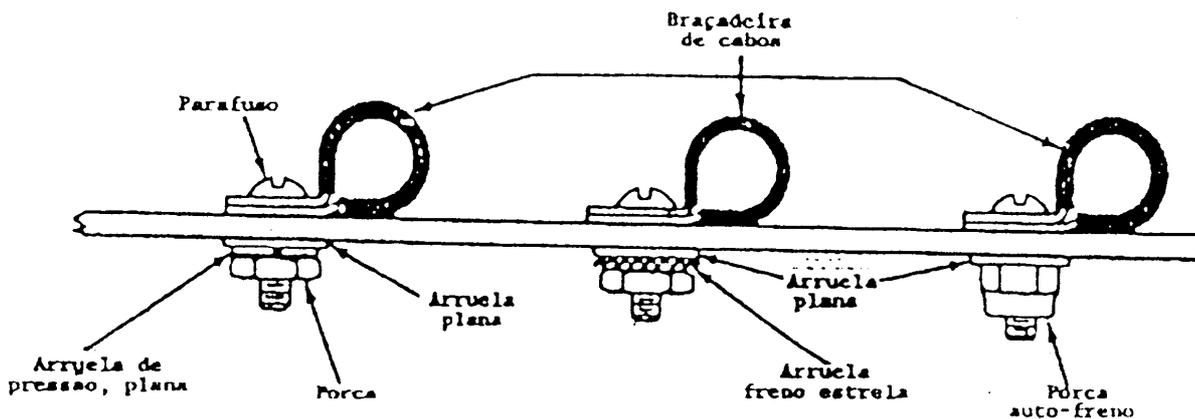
Ferragens típicas de montagem para braçadeiras de cabo
